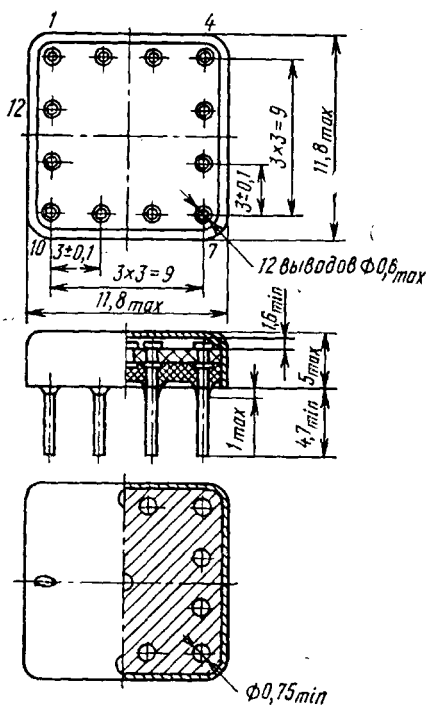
Конструкция металлополимерного корпуса «Тропа»
